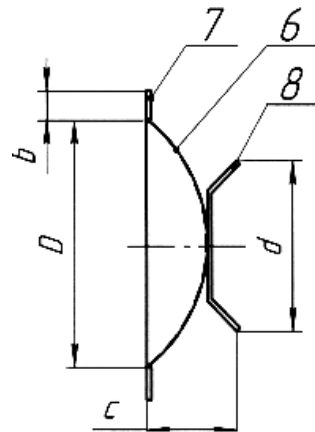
Схема размещения почвозацепов и дисково-лепесткового рыхлителя
